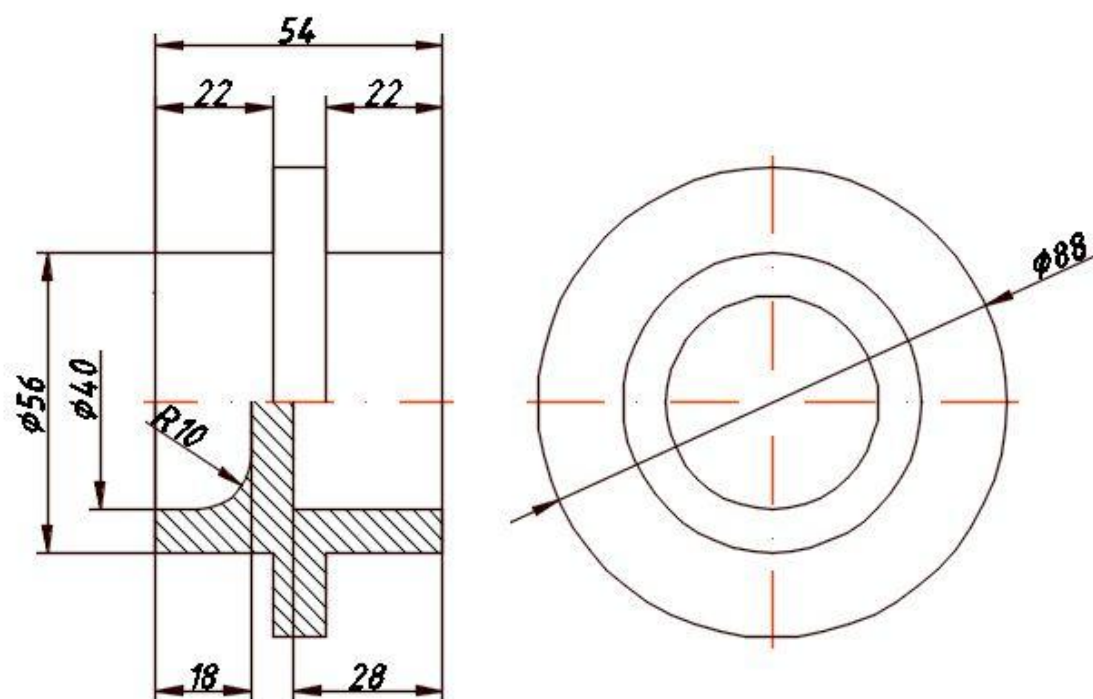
Рабочий чертёж опоры, выполненный в графическом редакторе
